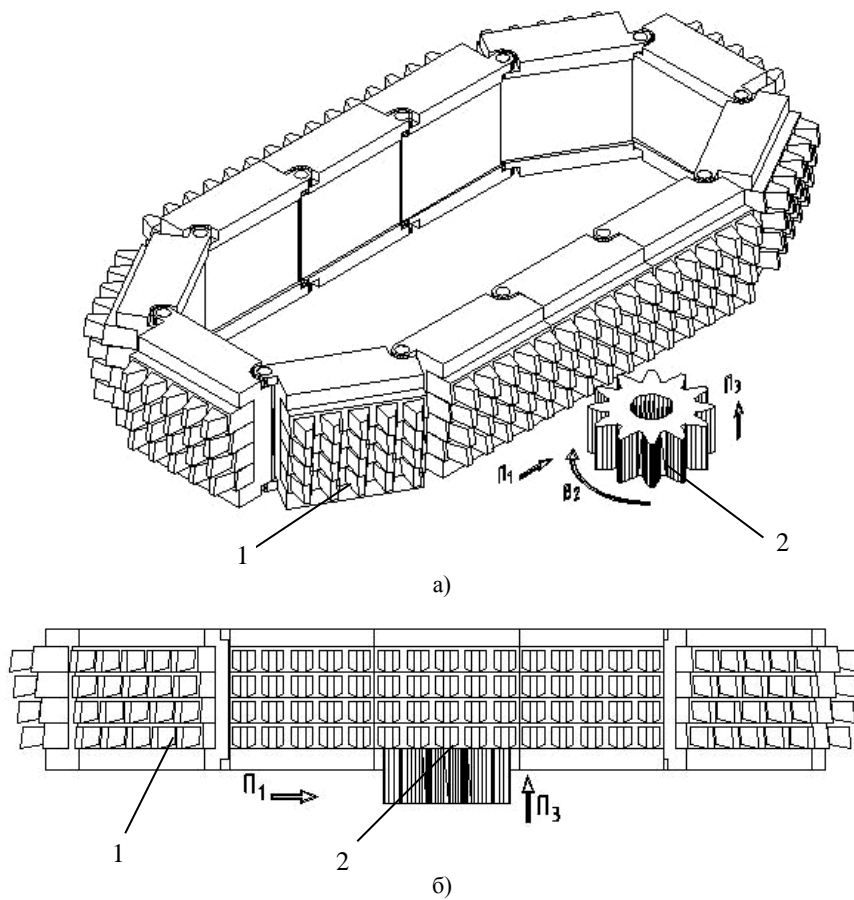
Схема зубопротягивания цепным инструментом реечного типа при осевой подаче заготовки
